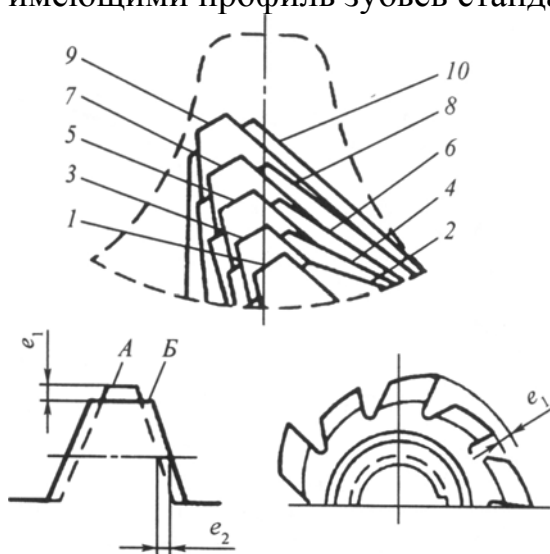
Последовательность срезания припуска во впадине колеса и профили зубьев ЧМФ с прогрессивной схемой резания и прямолинейными режущими кромками: А – профиль зубьев с нечетными номерами; Б – профиль зубьев с четными номерами
